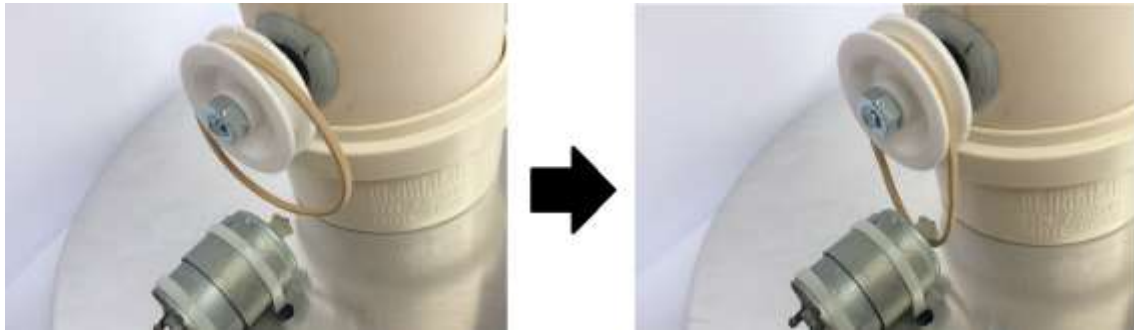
Acoplando a roldana do motor à roldana do rolete inferior do GVG. Fonte: O Autor.
